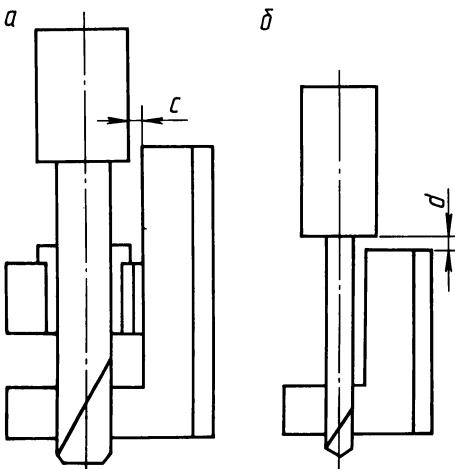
Расположение вспомогательного инструмента относительно обрабатываемой детали.
